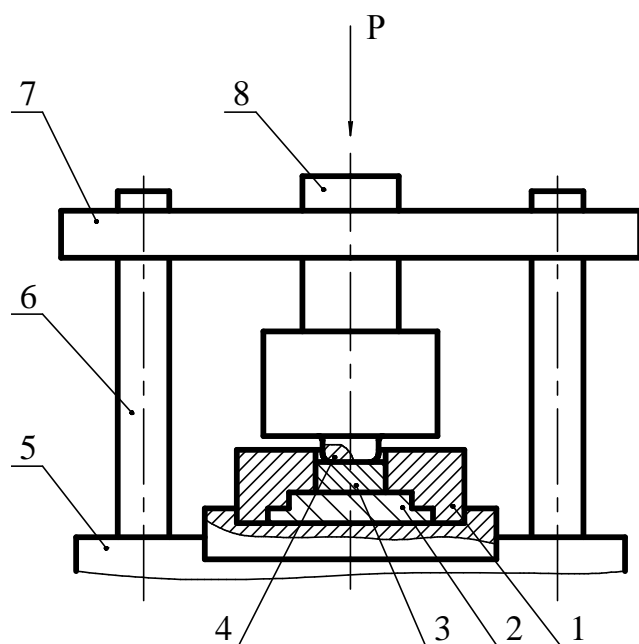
Штамп для градуировки точечных мессдоз: 1 - матрица; 2 - вставка; 3 - образец; 4 - мессдоза; 5 - основание; 6 - стойка; 7 - верхняя плита; 8 - пуансон
